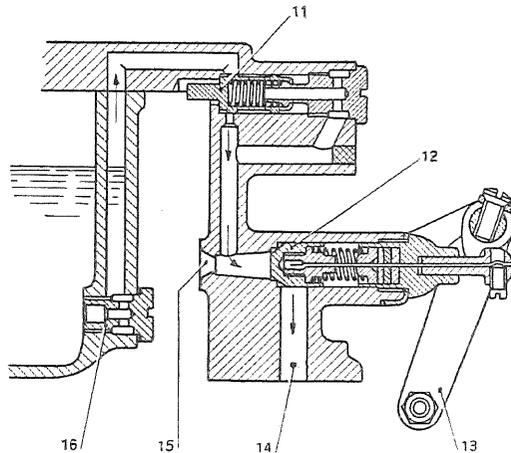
Sezione del dispositivo d'avviamento del carburatore Zénith 26 VF.
